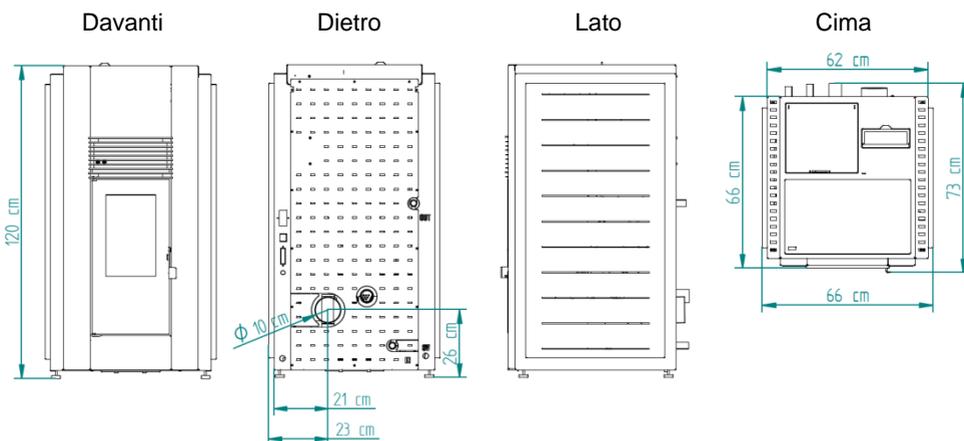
Dimensioni della stufa a pellet (versione acqua – Douro 23 kW)
